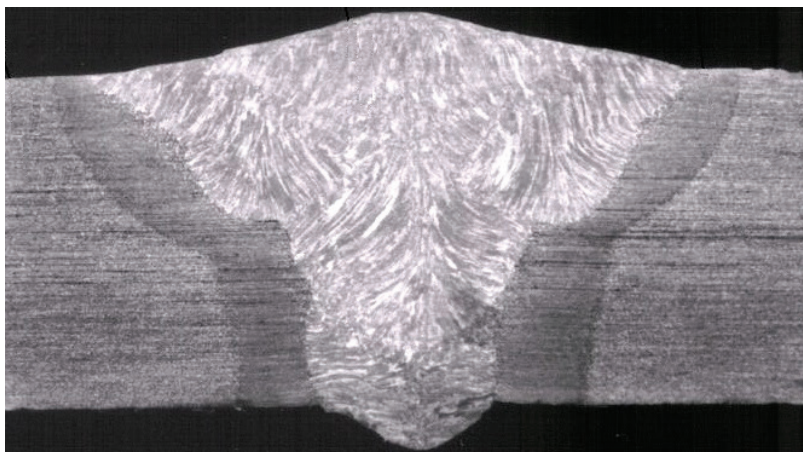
Структура шва и околошовной зоны при лазерной сварке
